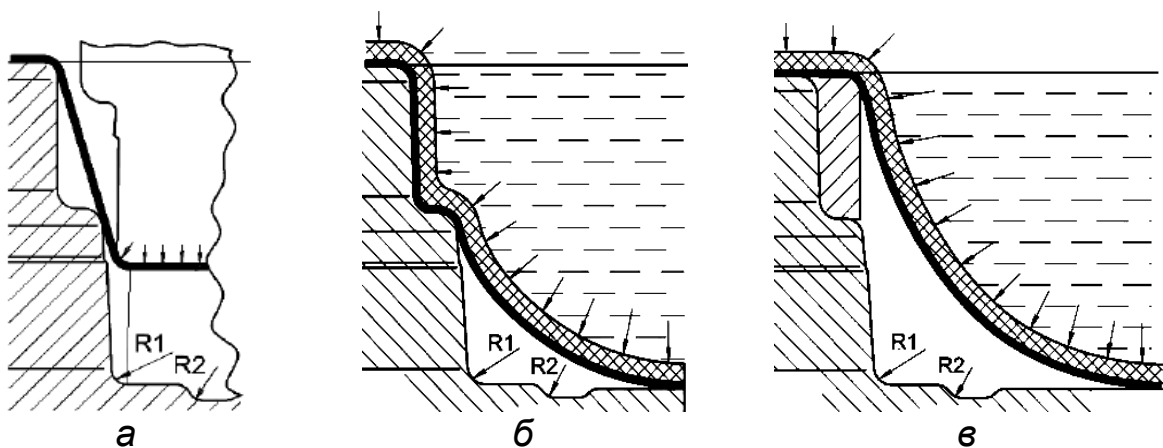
Формування ступінчастого борту і донних радіусів заготовки деталі:
